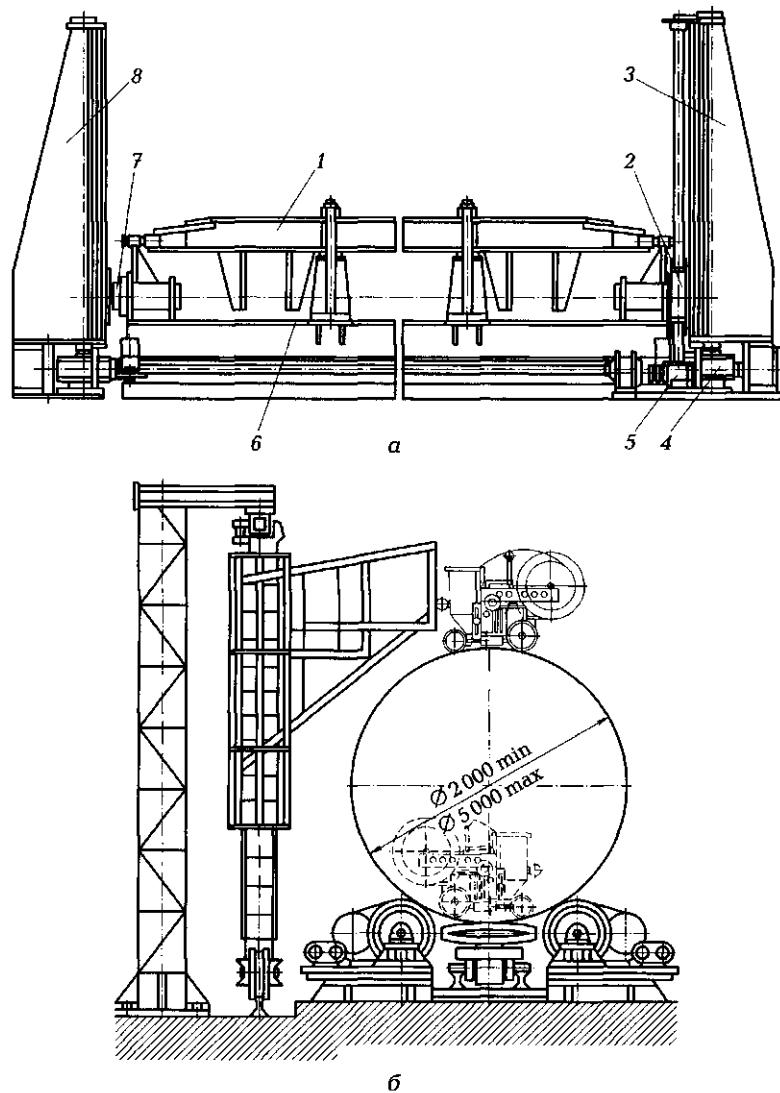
Приспособления для сборки и сварки:
